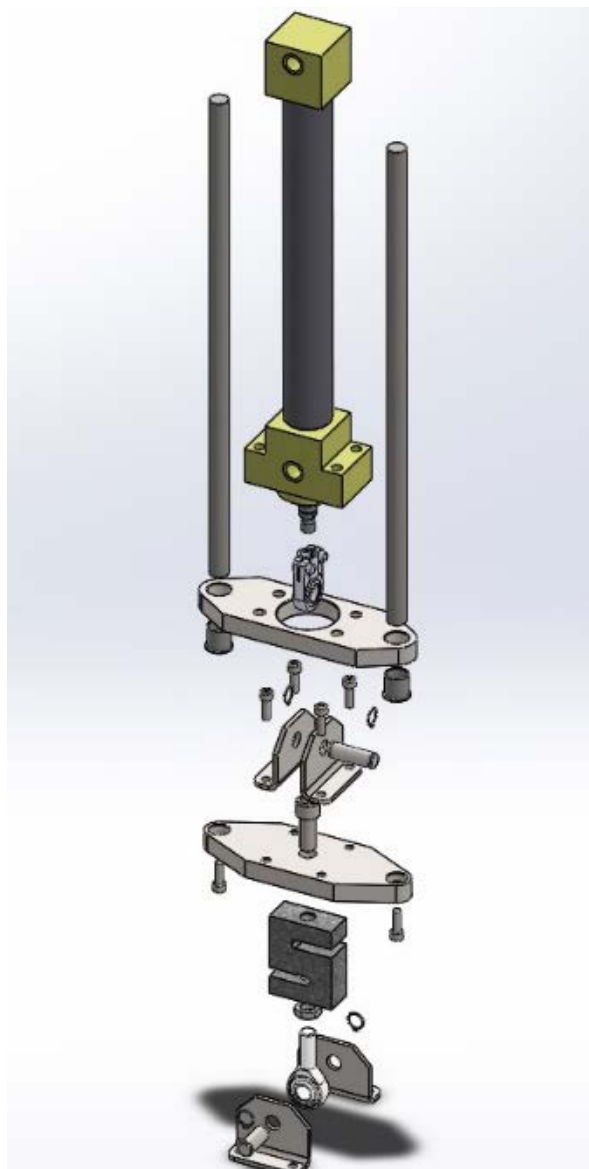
Vista explosionada del conjunto actuador y guía vertical
